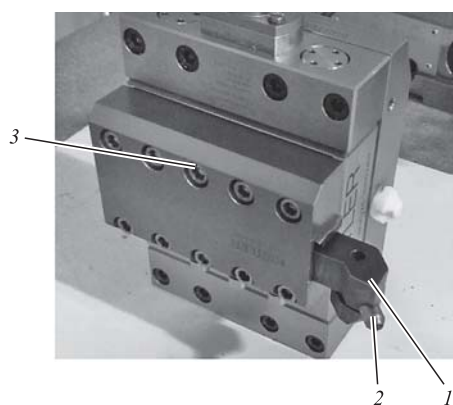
Подготовленный к выглаживанию инструмент, установленный в динамометрический комплекс Kistler Type 9129AA:
